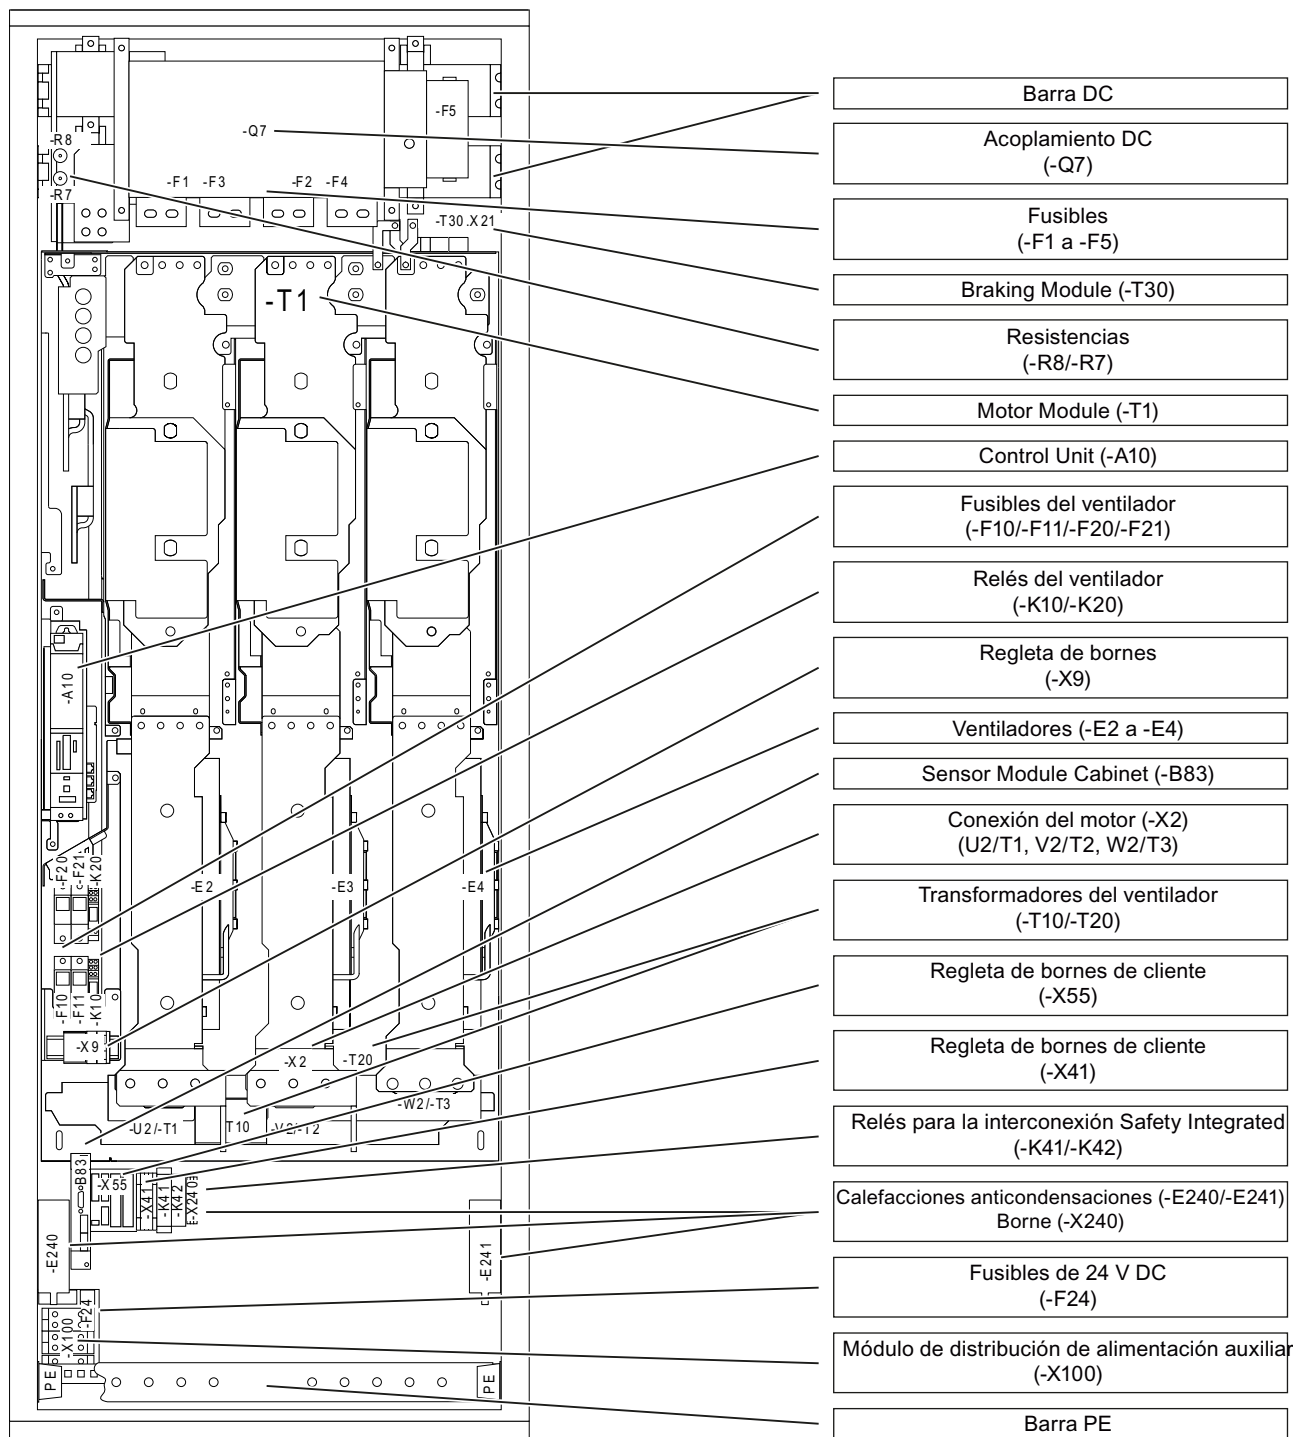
Diseño de Motor Module, diseño Chassis (tamaño JX)
